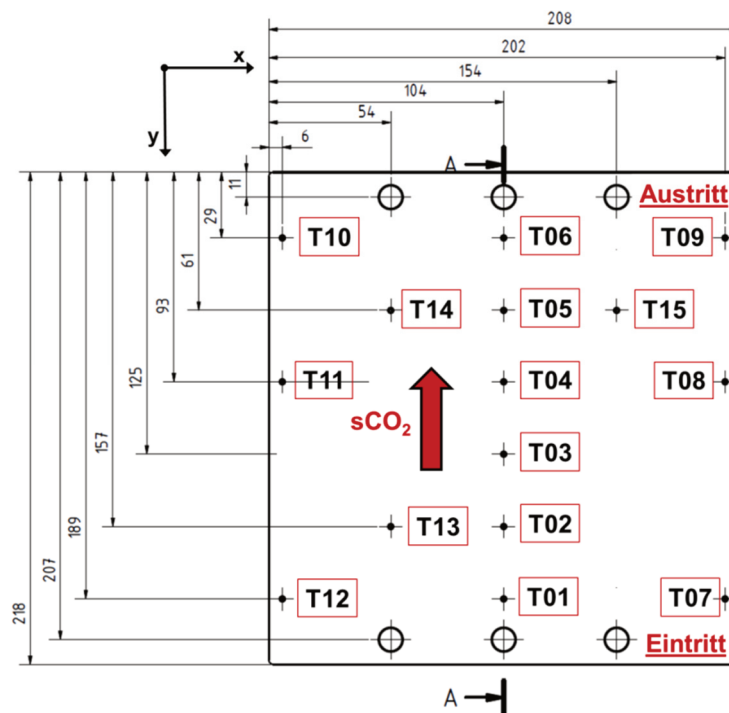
CAD-Zeichnung des DWHE im Endzustand mit Positionen und Bezeichnungen für die Dünnschicht-Pt-100.
